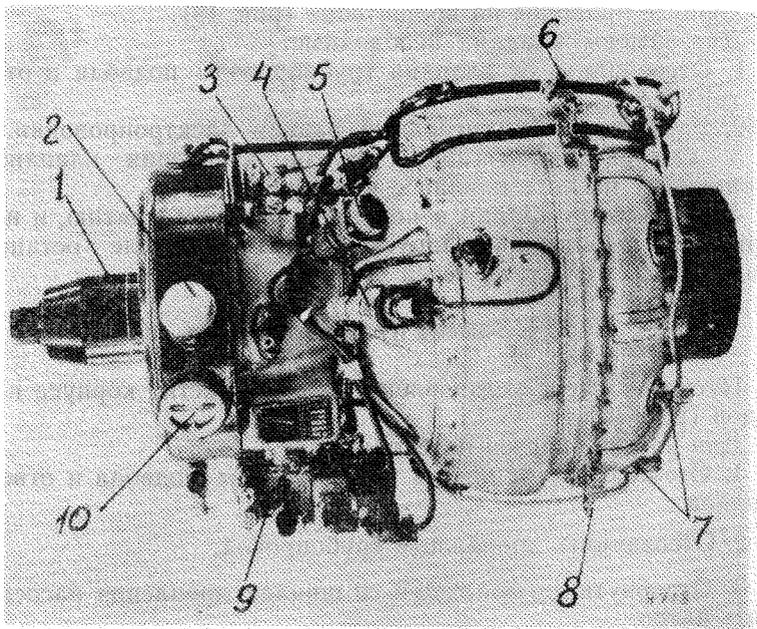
Расположение агрегатов на двигателе (вид слева):
